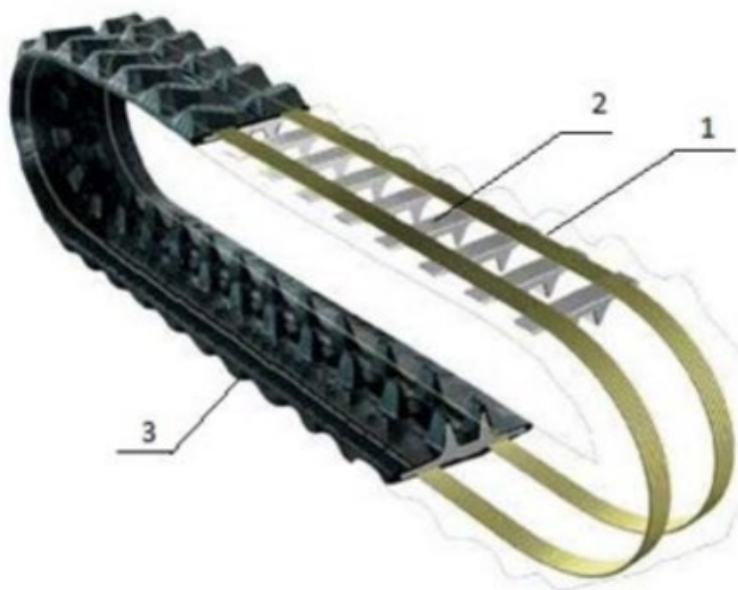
Конструкция резиноармированной гусеницы: 1 — металлокорд; 2 — стальной сердечник; 3 — резиновый массив [140]
